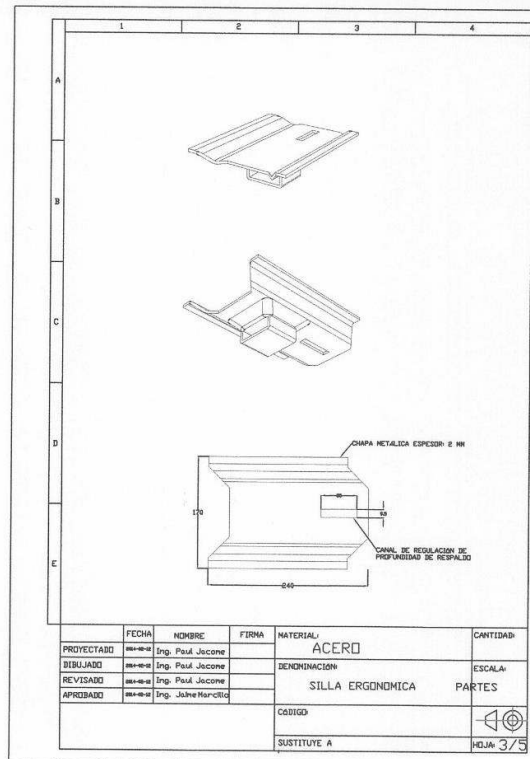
Plano de construcción soporte regulable para asiento
